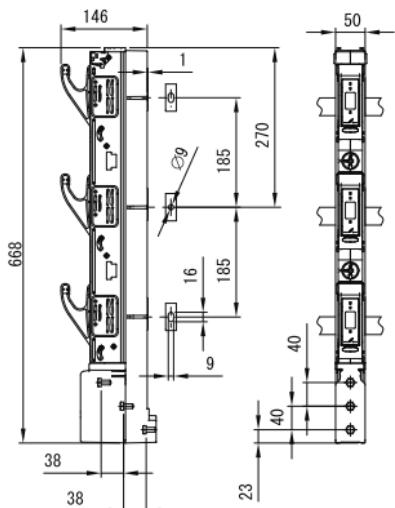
Габаритные размеры ПВР-3 160 А / Figure A.2 – Overall dimensions of PVR-3 160 A
